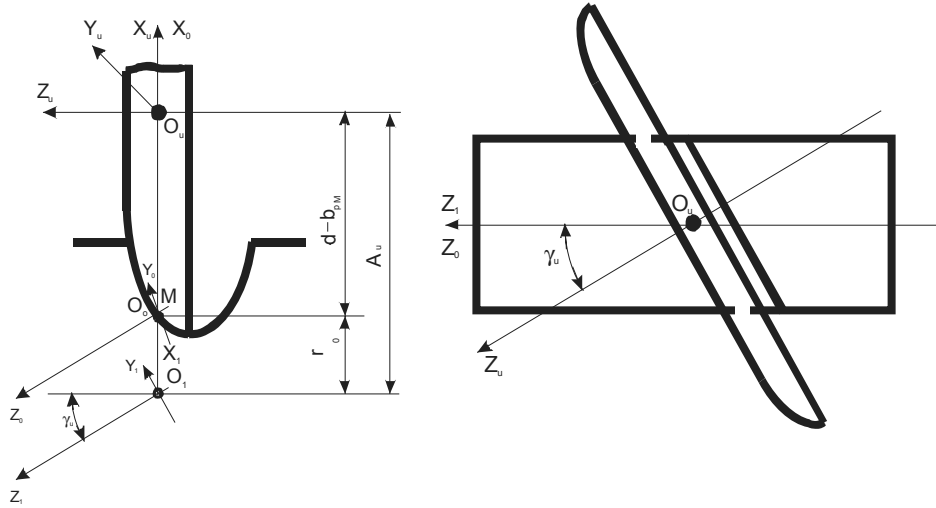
Розташування шліфувального круга при обробці поверхні черв'яка
